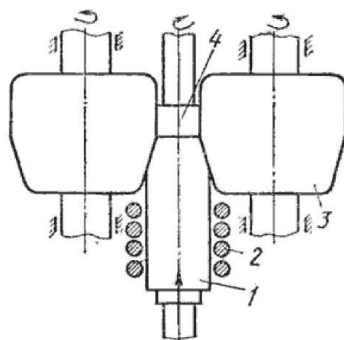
Схема прокатки шестерни с осевой подачей заготовки
